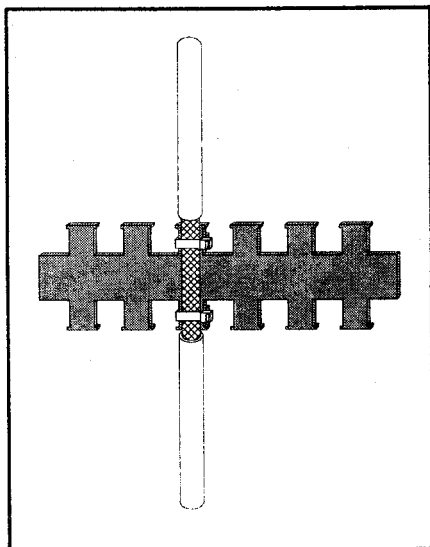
в: Металлический шланг или соединительный элемент кабеля на металлической неокрашенной гребенчатой/зубчатой шине
